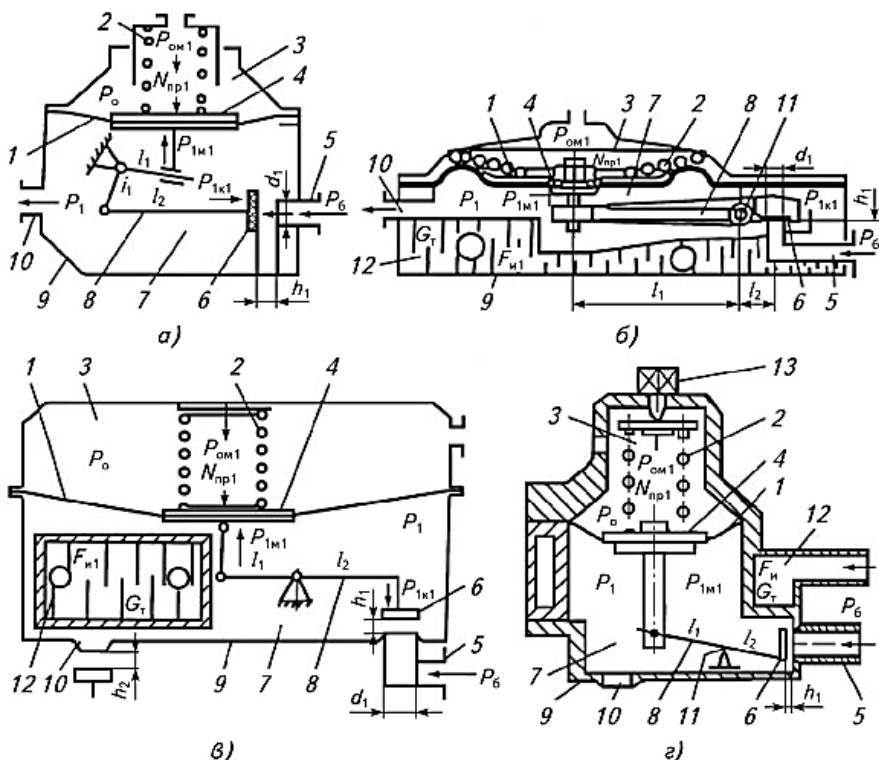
Розрахункова принципова схема першої ступені газового редуктора з важільною системою передачі зусиль.
